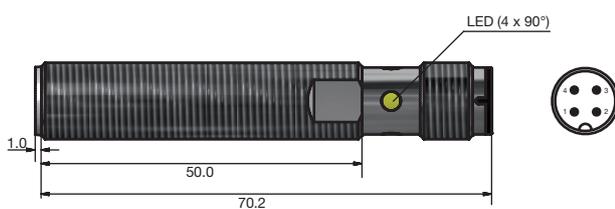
Lange Ausführung, Quasi-bündiger Einbau, Steckversion
